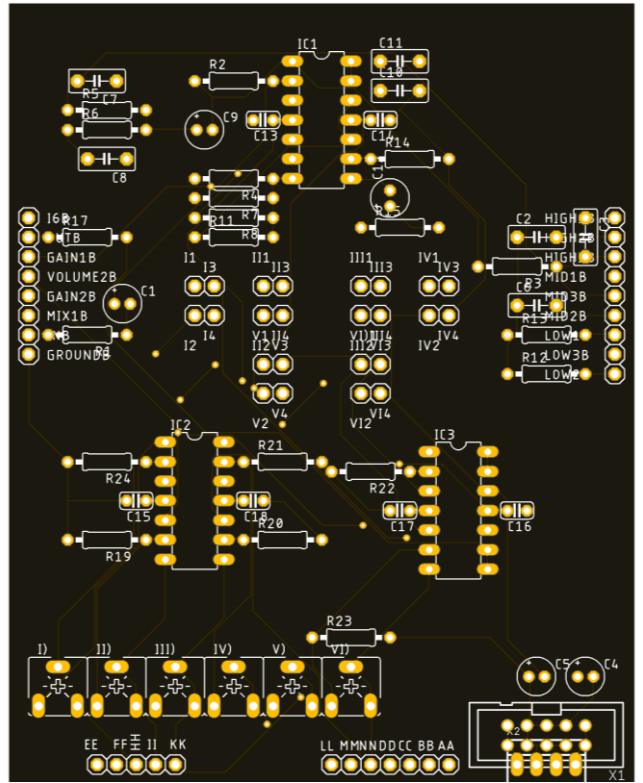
Board Layout: Pots&Sockets PCB
